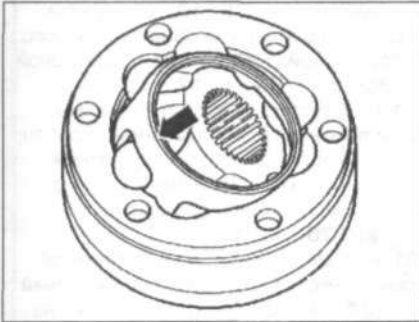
Вставьте ступицу с шариками в корпус шарнира (стрелка).
